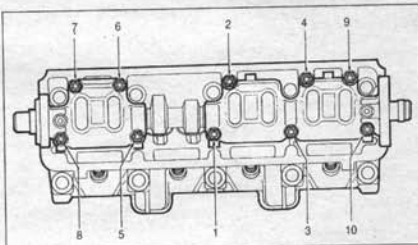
Порядок затягивания гаек крепления корпусов подшипников распределительного вала
